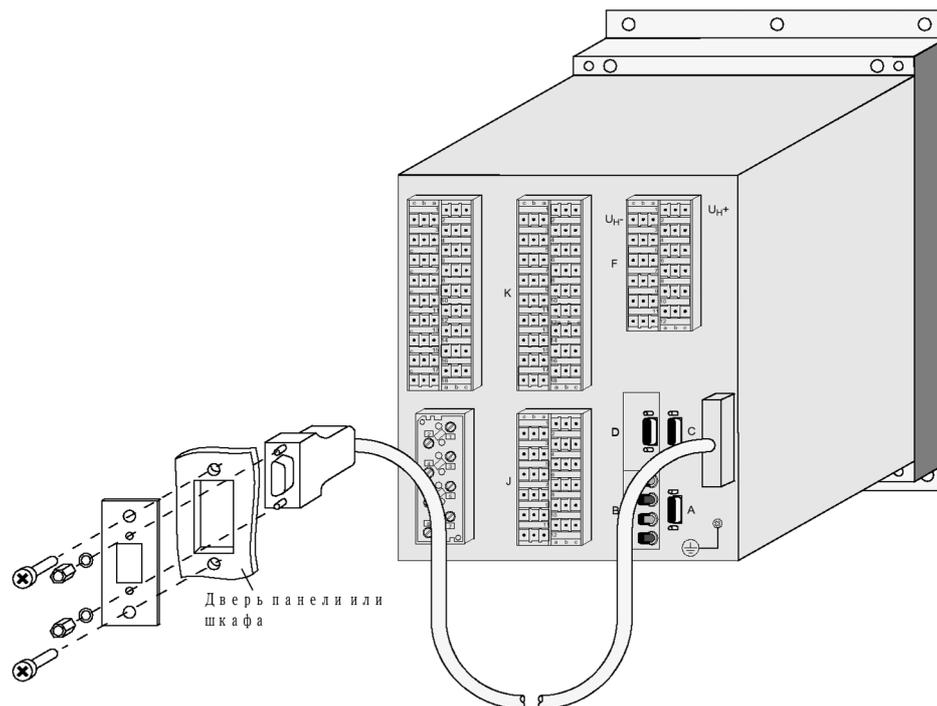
Закрепление сверхминиатюрного разъема кабеля с аппаратной защитой на панели управления или двери шкафа (пример для корпуса  $1/2$ )
